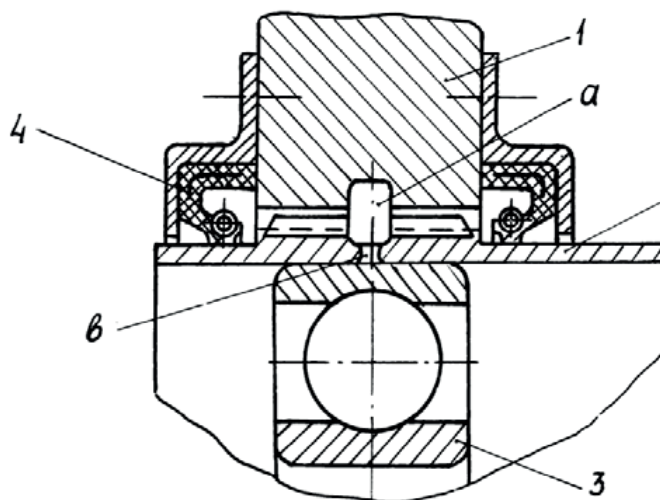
Конструкция узла зацепления ВЗП с дополнительной полостью для пластичной смазки и отверстиями для подпитки пластичной смазкой сочленения гибкого колеса с гибким подшипником (позиции в тексте)
